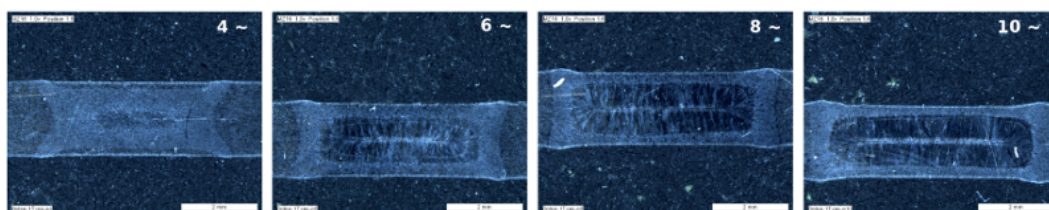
Cinétique expérimentale de développement du noyau - assemblage 1T XES 2mm - 0 point soudé.
